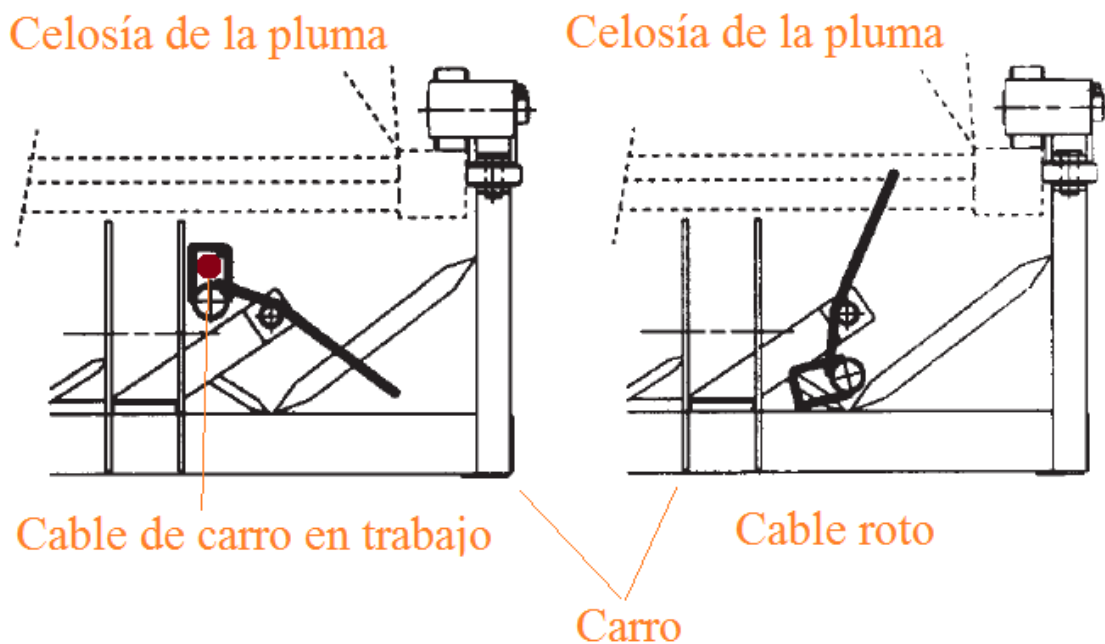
Detalle sistema bloqueo carro por rotura de cable
